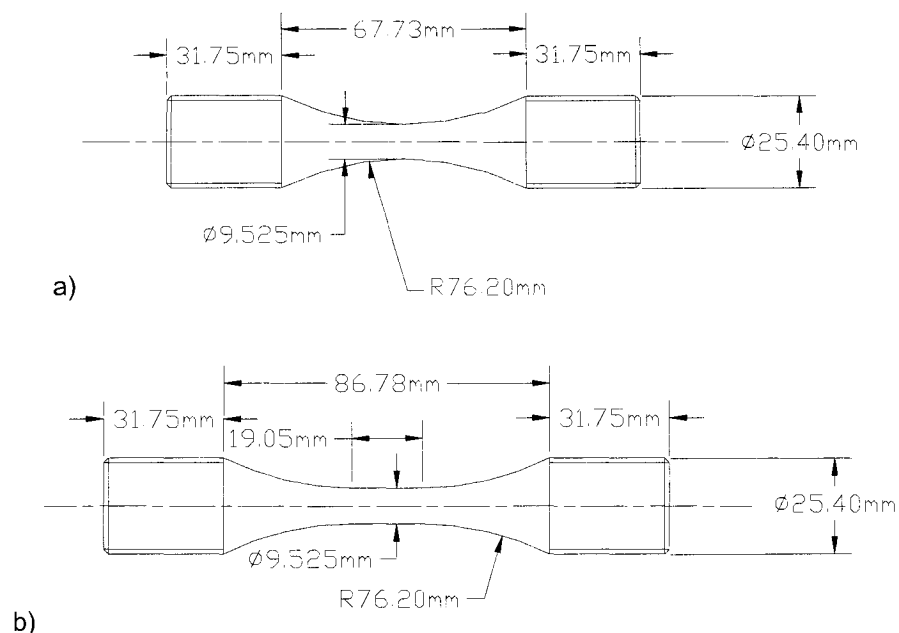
3. Géométries des éprouvettes de fatigue à fût (a) toroïdal et (b) cylindrique
